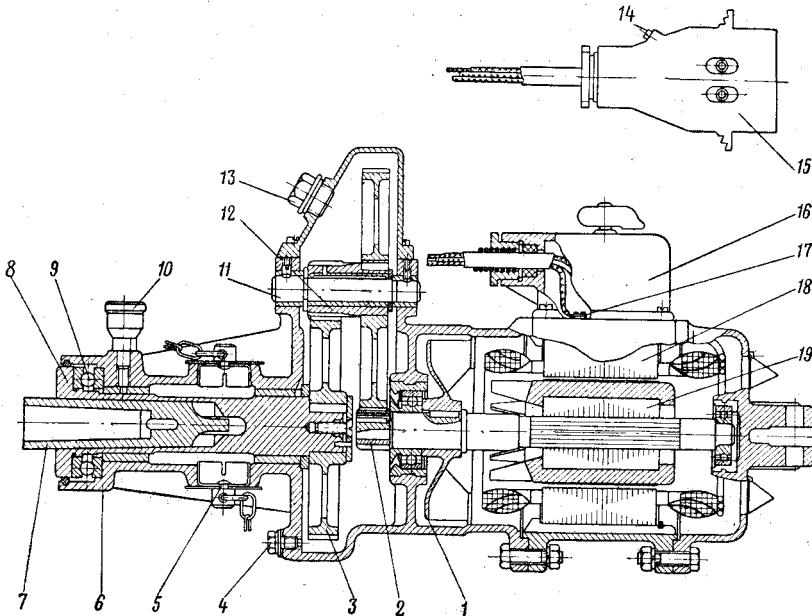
Мотор-редуктор рельсосверлильного станка 1024Б:
